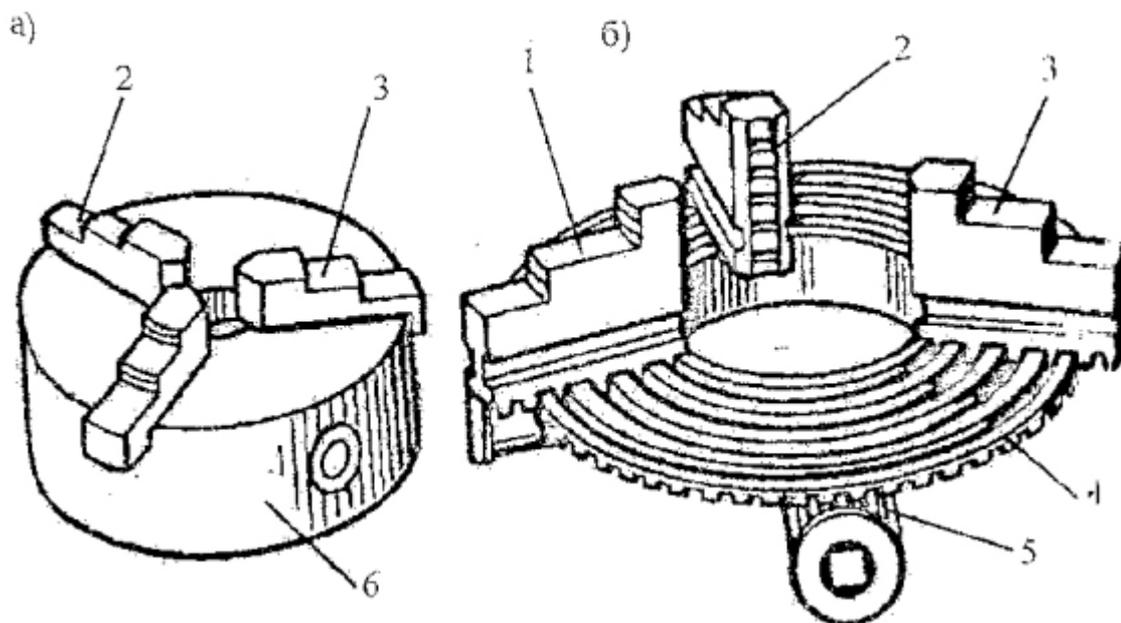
Самоцентрирующий трехкулачковый патрон: а – его общий вид;
